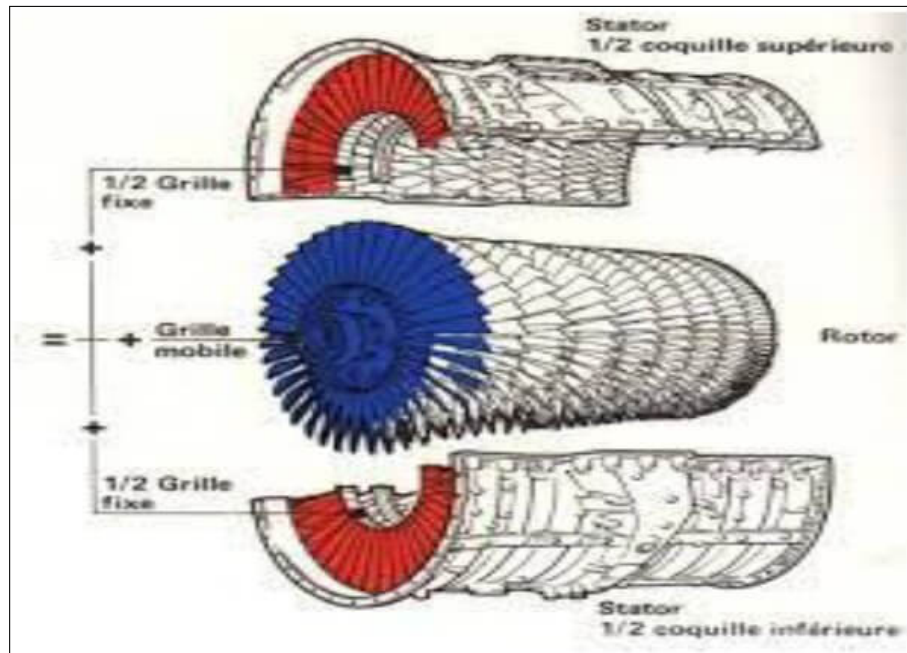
Schéma représente le Rotor et le Stator d'un compresseur axial [2]
